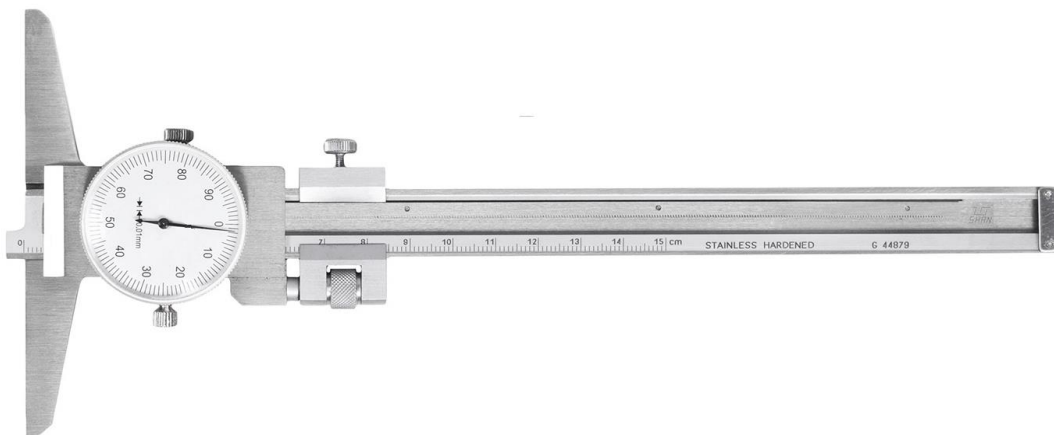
Общий вид штангенглубиномеров ШГК с прямой штангой
